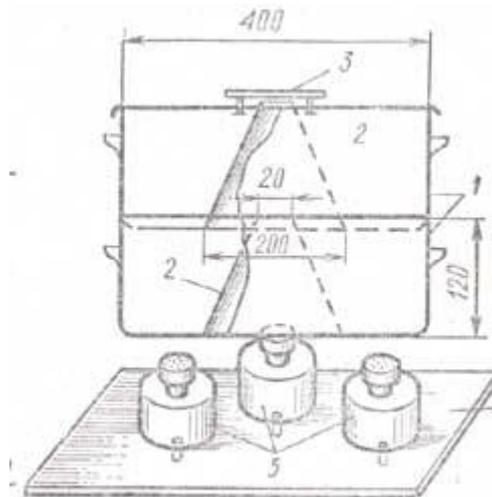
Варочная установка типа «самовар» (1—кастрюли; 2—приваренный конус; 3 — крышка-подставка; 4— подставка; 5 — примусы)
